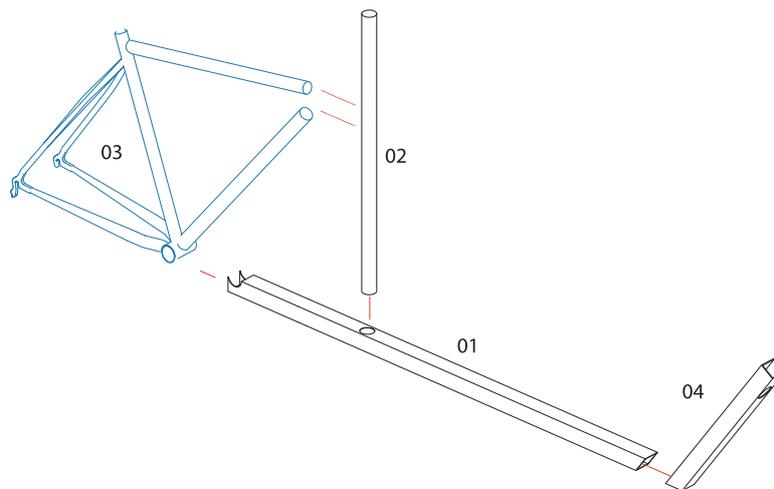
Explosionszeichnung des Grundrahmens; Quelle: [1]
